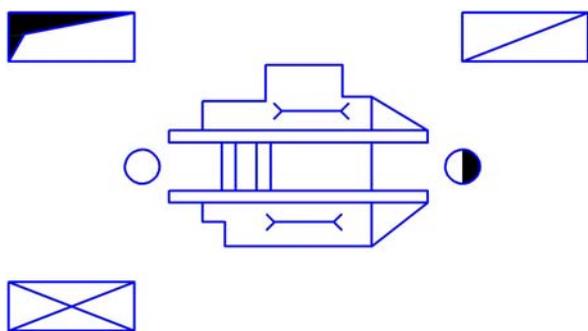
Организация рабочего места станка Ц2К20 концевальной общего назначения для поперечного раскроя заготовок одновременно с двух торцов
